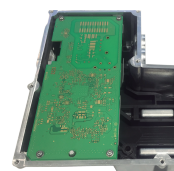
Détail partiel d'un assemblage de PCB sur aluminium pour un On-Board-Charger.
